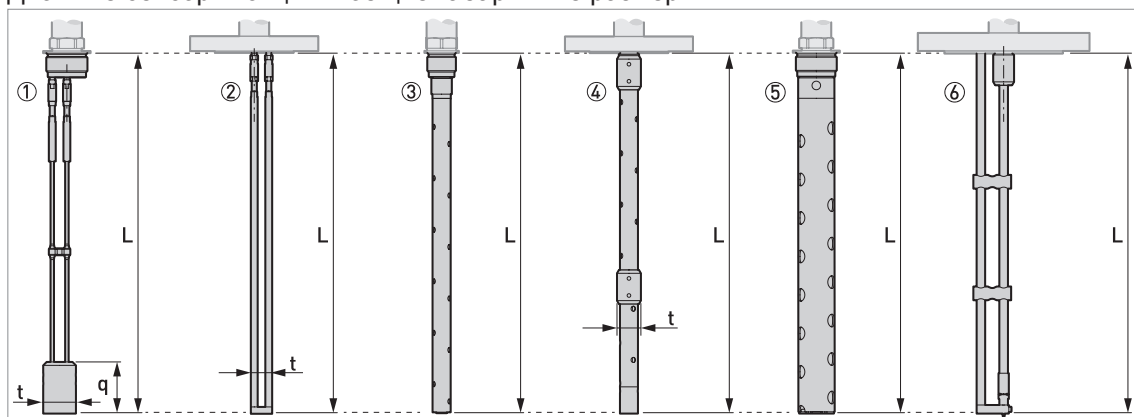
Двойные сенсоры: опции и общие габаритные размеры
